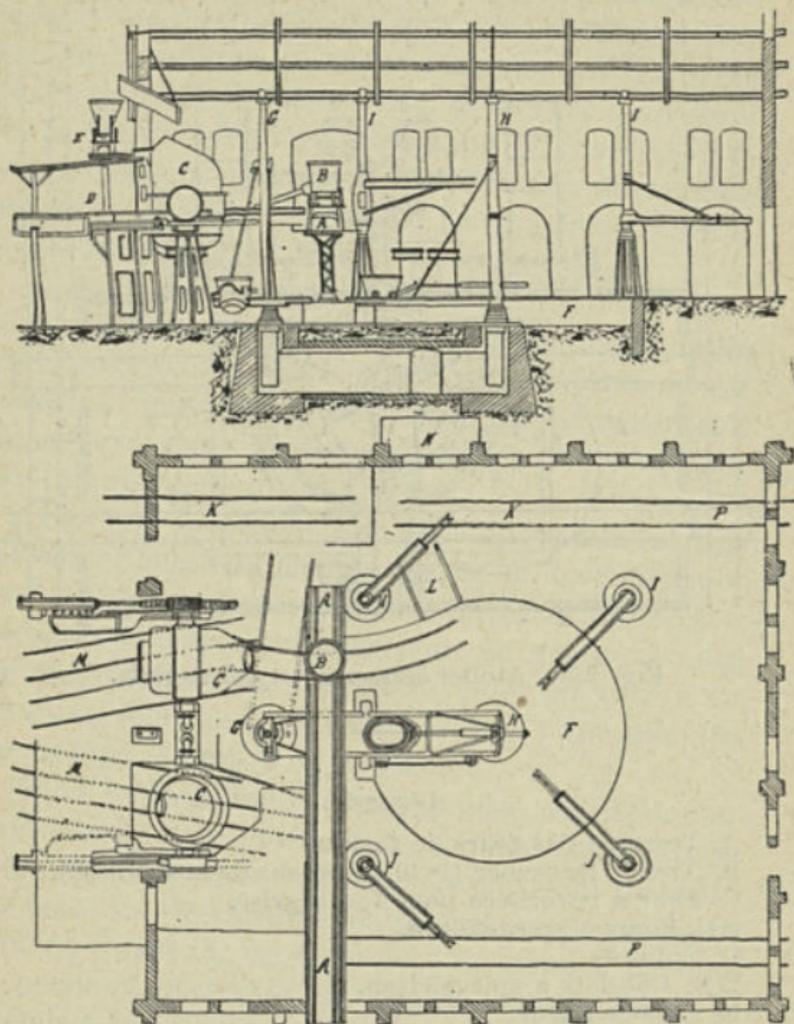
et 240. Plan et coupe d'un atelier Bessemer, type américain.
